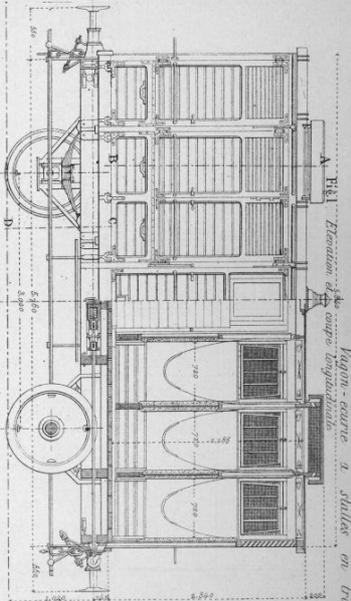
à 3. Wagon couvert à stalles ou travers (travers Fig. 1 à 3.)
